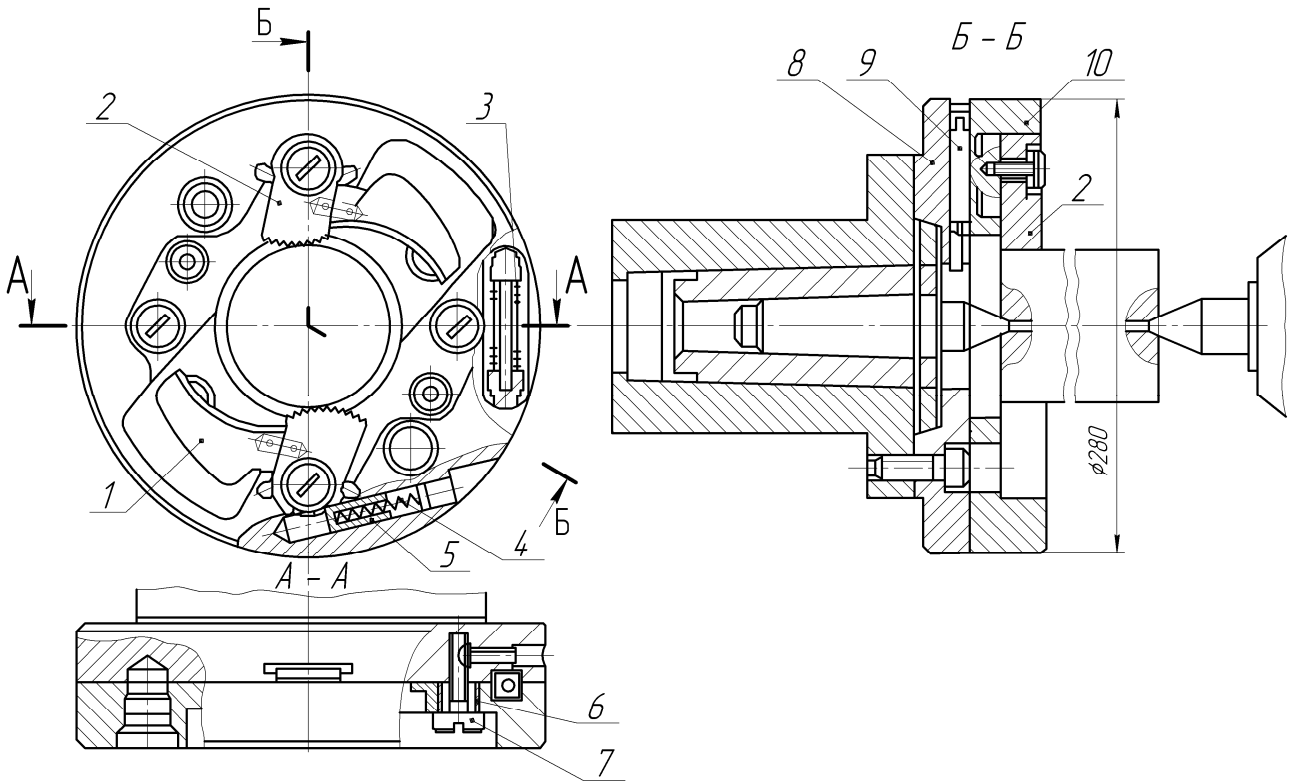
Будава повідкового патрона з двома ексцентриковими кулачками: 1 – вантаж; 2 – кулачок; 3, 4 – пружини; 5 – штовхач; 6 – розпірна втулка; 7 – гвинт; 8 – фланець; 9 – ведучий палець; 10 – корпус патрона
